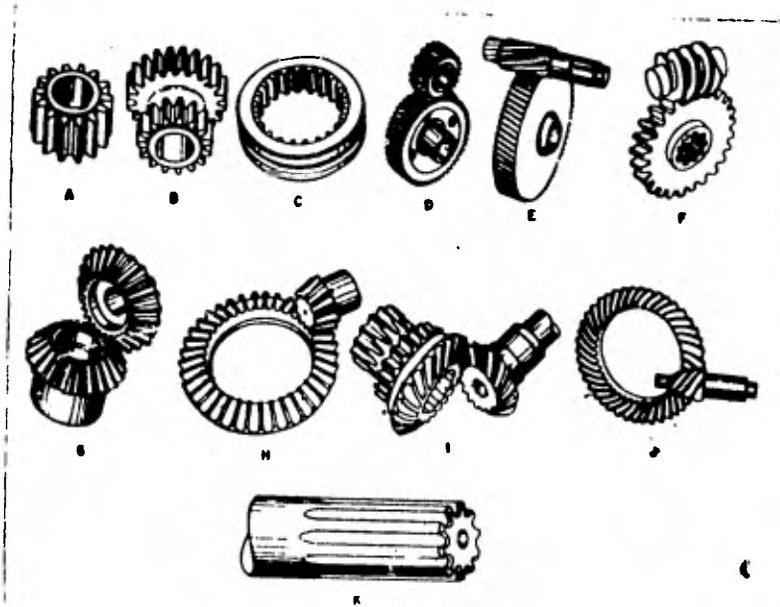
Tipos de engranajes: A, piñón. B, desplazable. C, corona de dientes interiores. D, engranaje con dientes en flecha o espina de pescado. E, Engranaje helicoidal. F, tornillo sin fin y corona. G, engranaje cónico en inglete. H, corona y piñón cónicos. I, engranaje cónico helicoidal empleado en los tractores. J, piñón y corona hipoides. K, extremo ranurado deslizante de un árbol de transmisión.
